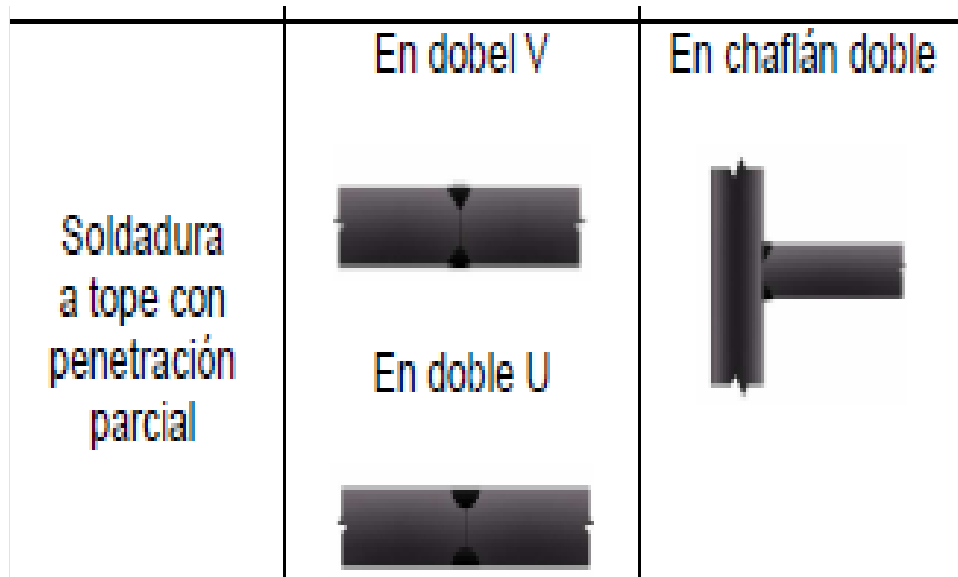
Soldadura a tope con penetración parcial
